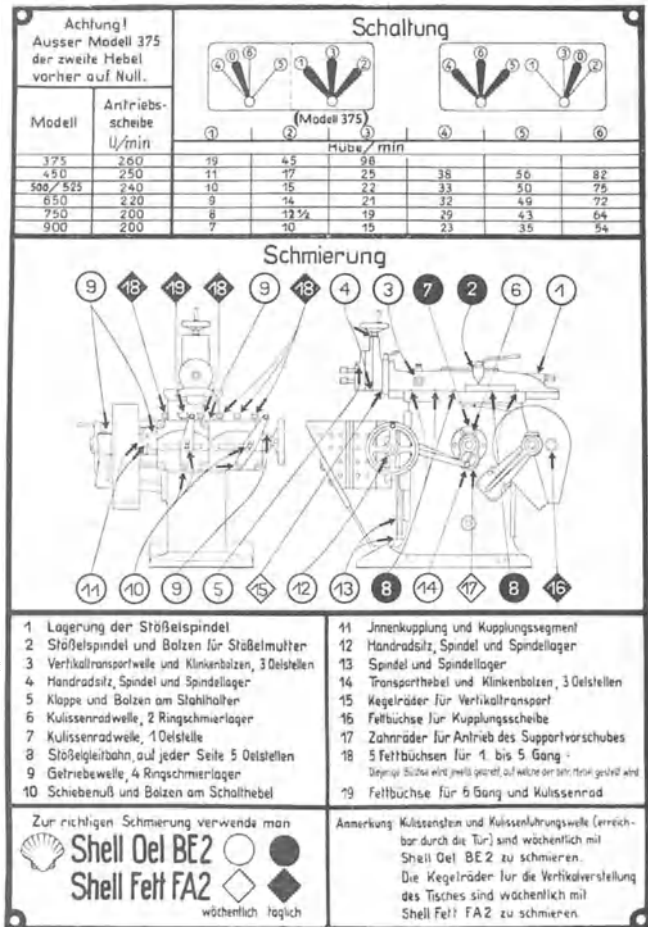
Beispiel einer Schmieranweisung für eine Shaping-Maschine.
